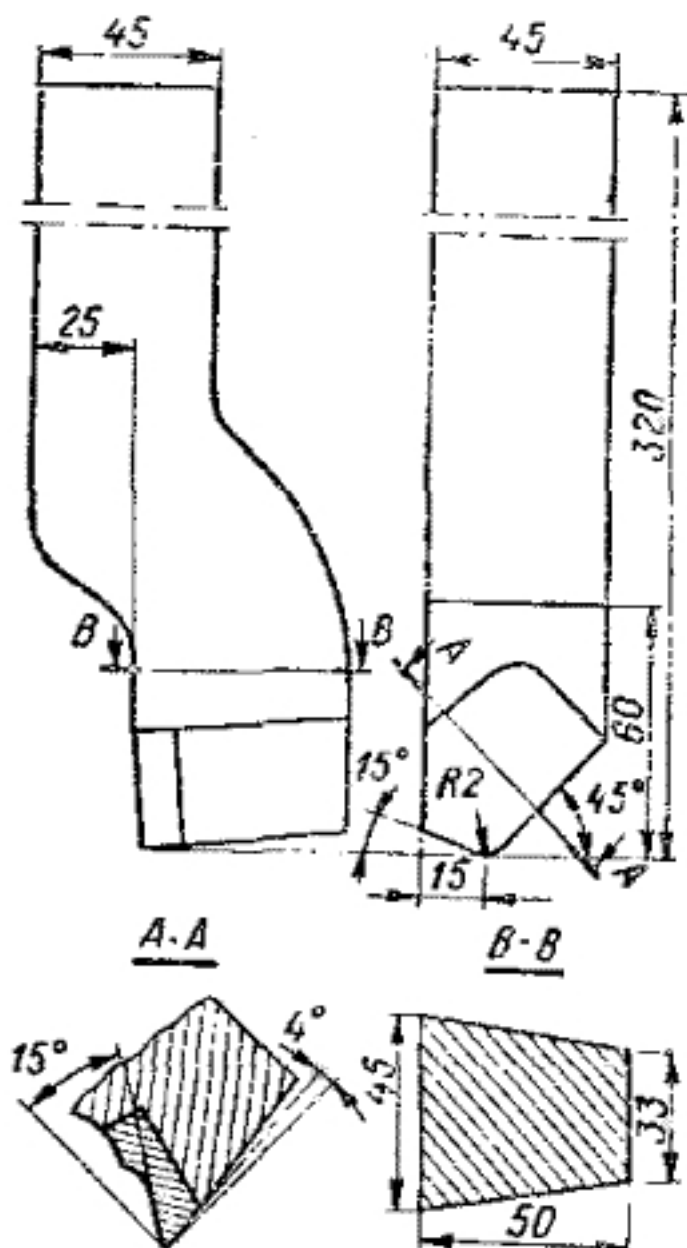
Резец для тяжелых работ конструкции Д. Н. Преснова (а) и схема врезания в металл обычного строгального резца и резца Д. Н. Пресно-
